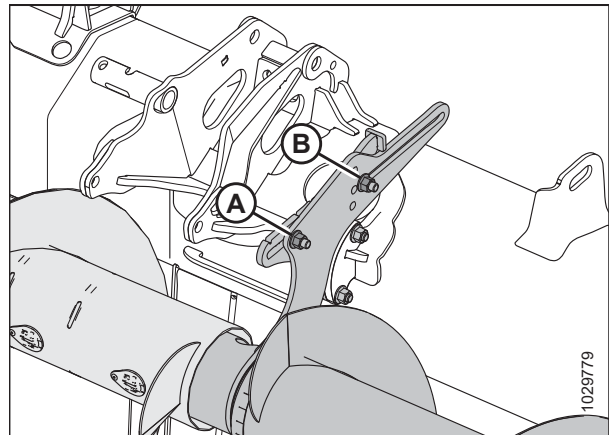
Ursprüngliche Einbaustellung – dreiteilige Schnecke
